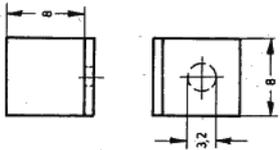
Befestigungswinkel, 2 ohne Bohrung, 7 mit einer Bohrung, 2 mit zwei Bohrungen.
